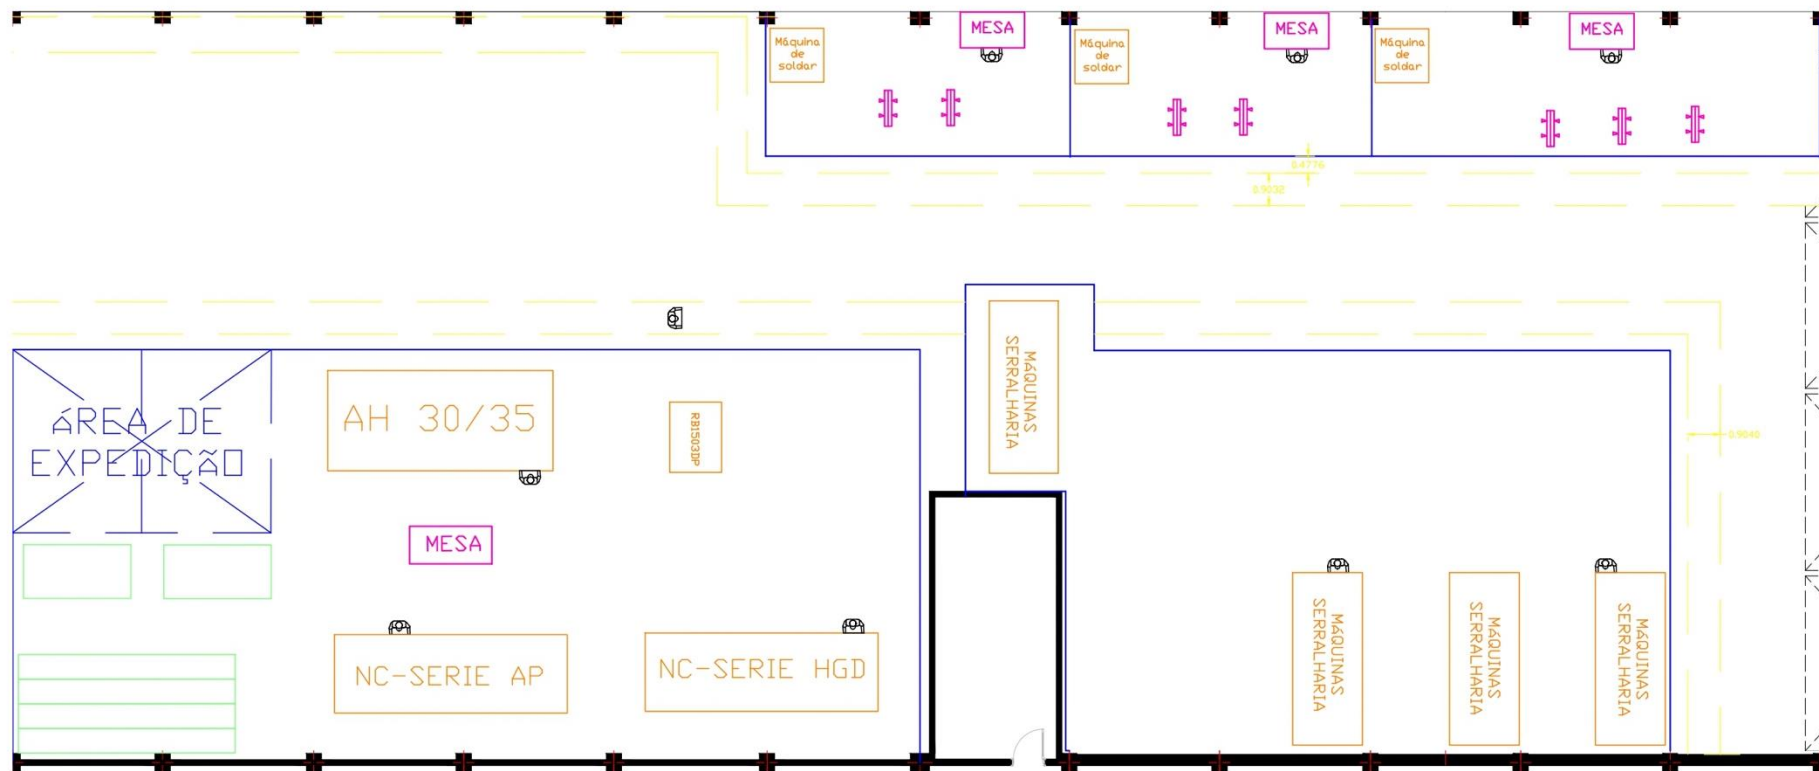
Corte da Secção de Estruturas Metálicas
